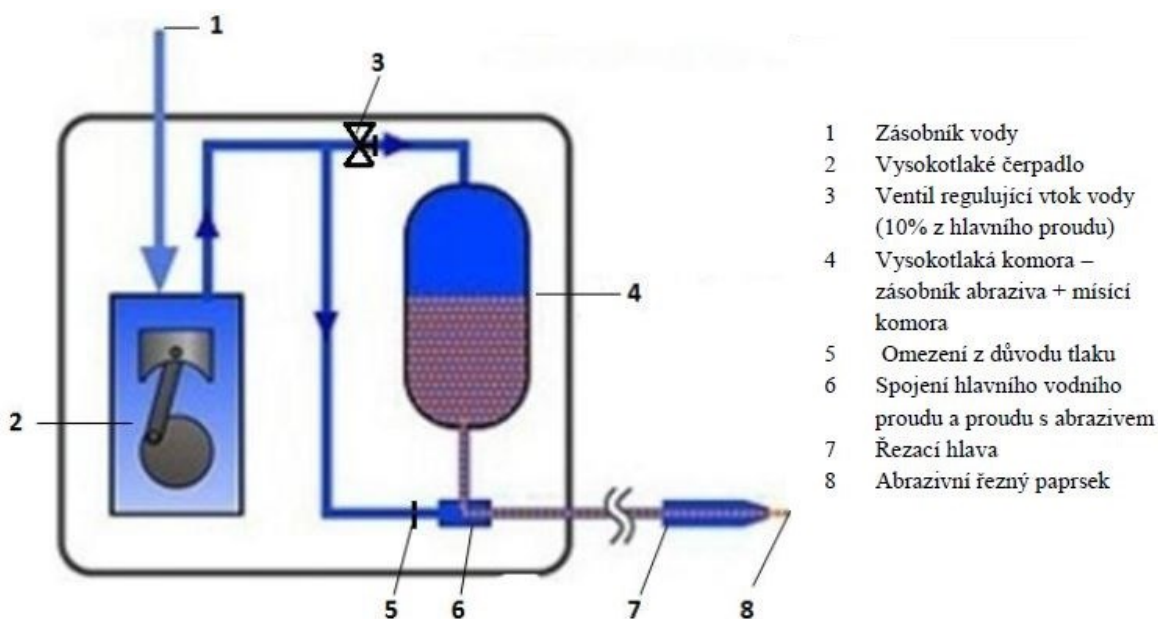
princip vzniku abrazivního vodního paprsku [14]
